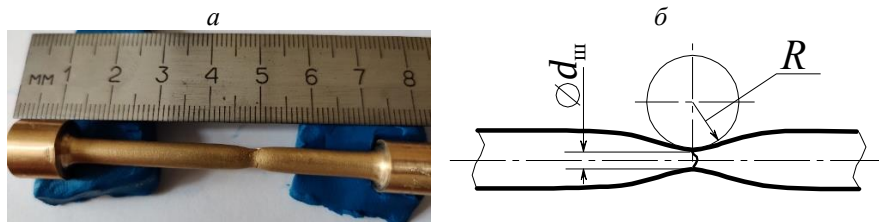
Подготовка к измерению (а) и схема измерений (б) шейки разорванного образца
